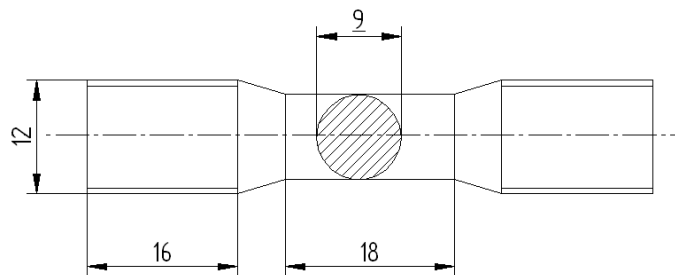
Eprouvette pour essais de fatigue cyclique sur la machine MFC, dimensions en mm.
